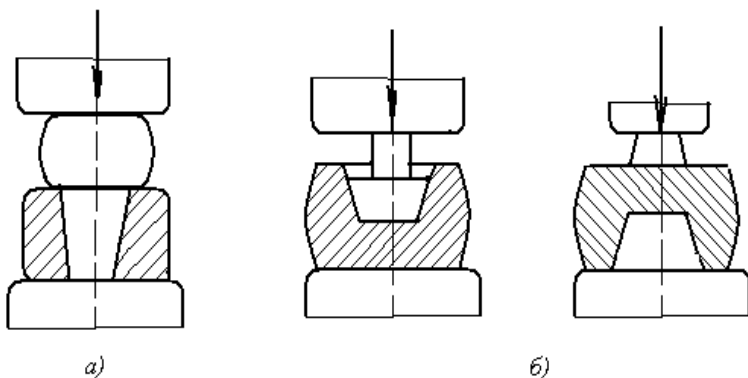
Схема операций высадки (а) и двусторонней прошивки (б)
